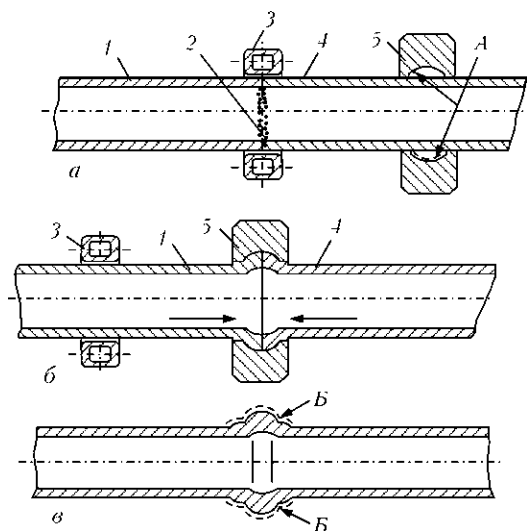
Схема процесса индукционной сварки и сваркопайки труб с принудительным формированием шва: а, б — соответственно процесс нагрева и осадки; в — полученное сварное соединение: 1, 4 — трубные заготовки; 2 — смесь материалов для пайки и сварки; 3 — кольцевой индуктор; 5 — формирующее устройство; А — формирующая поверхность устройства; В — поверхность валика шва
